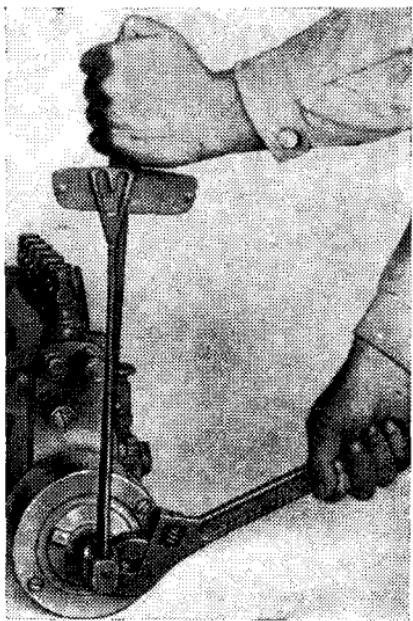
Затяжка гайки крепления автоматической муфты опережения впрыска топлива
